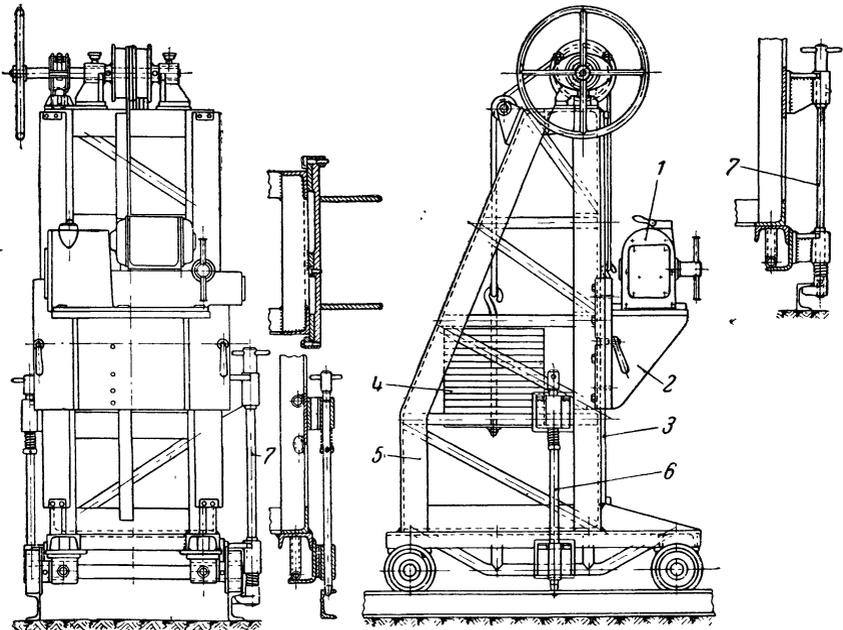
Станок для разделки отверстий в корпусе фюзеляжа.
